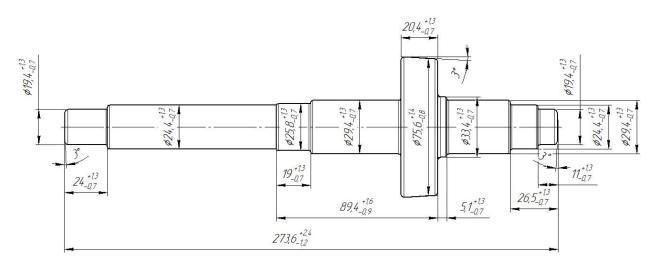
Штамповка детали «Фланцевый вал»
